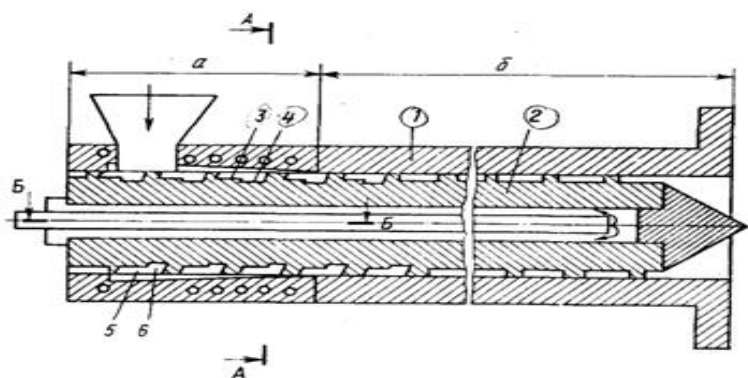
Приспооба для підготовки а саме змішування.
